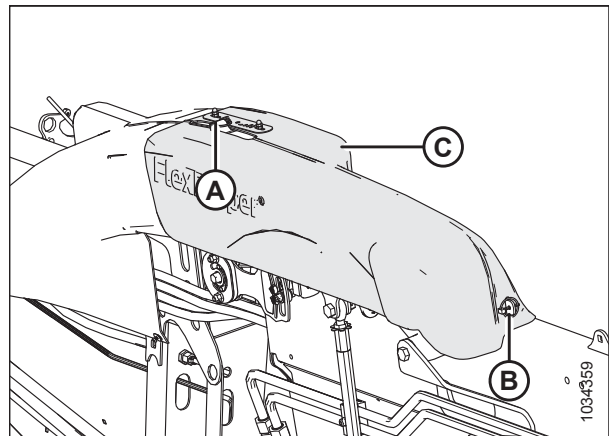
Cubierta de conexión de flexión: lado izquierdo
